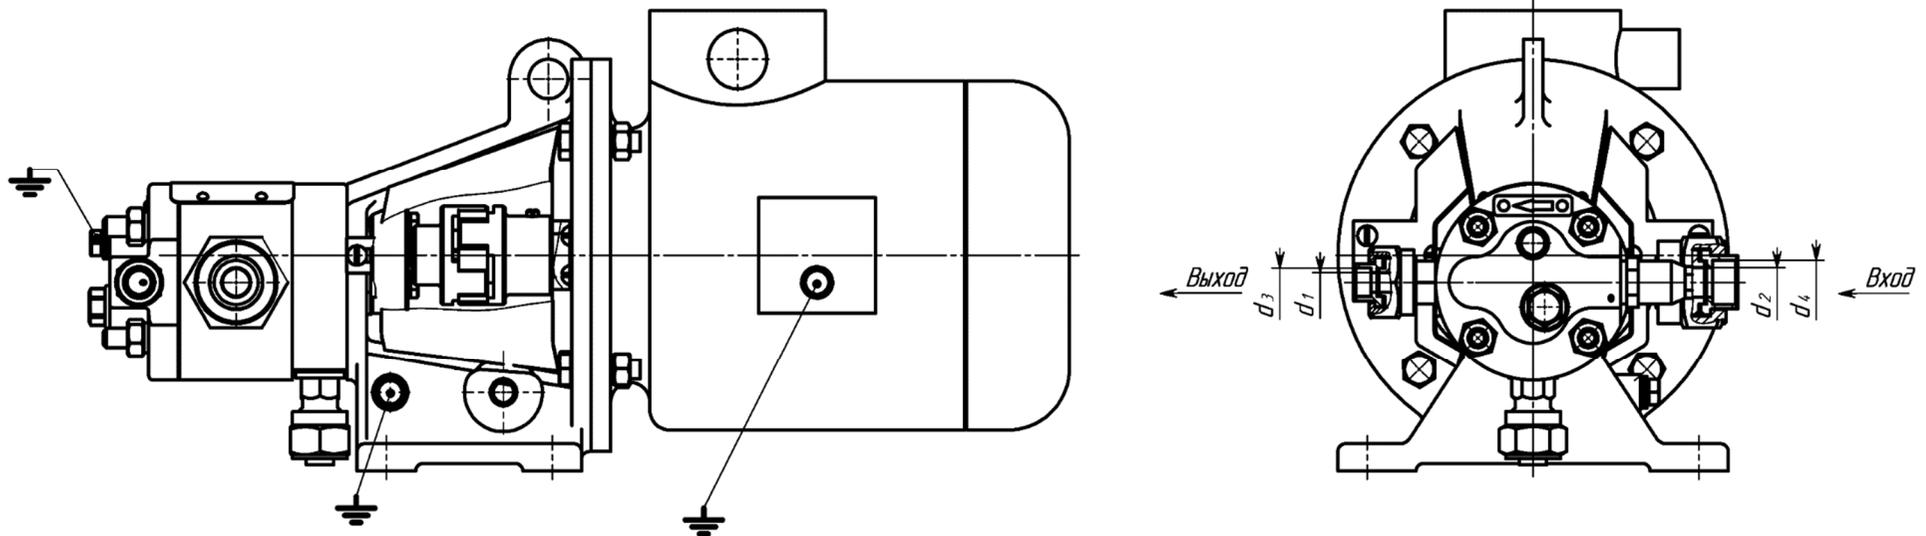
Габаритный чертеж агрегата типа НМШФ с правым вращением ведущего ротора.
